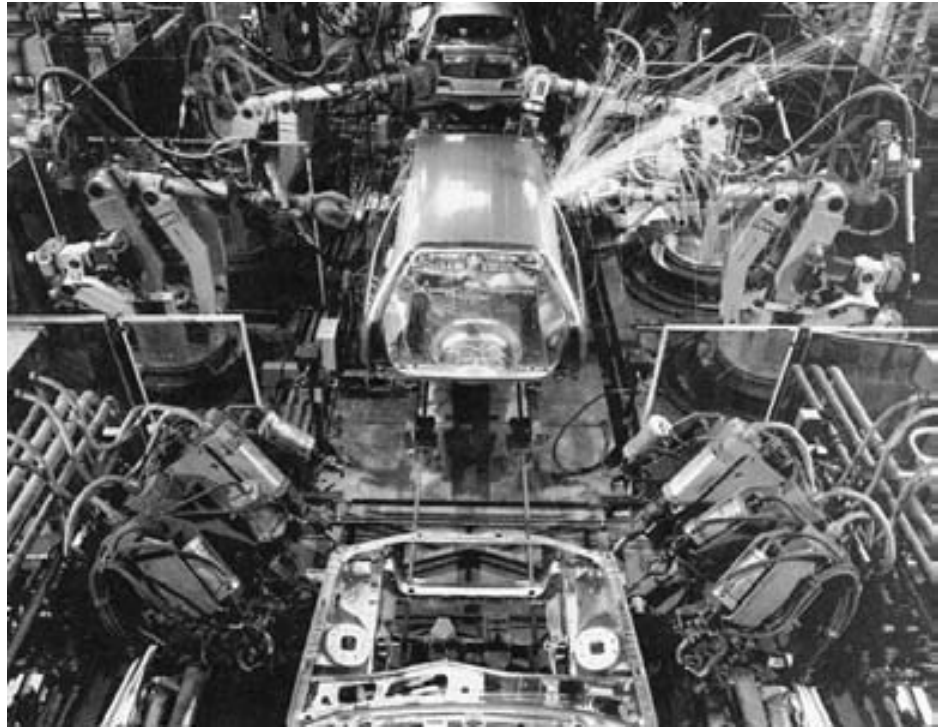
Parte de una línea de ensamble automotriz en la cual los robots ejecutan operaciones de soldadura de puntos. (Foto cortesía de Ford Motor Company).
